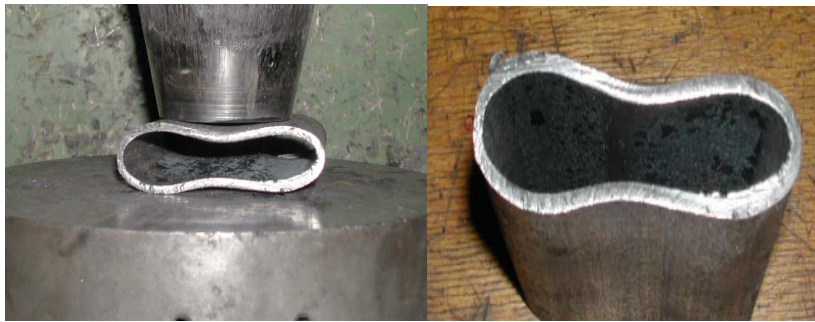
Tube aplatie Machine de l'aplatissement [12].
